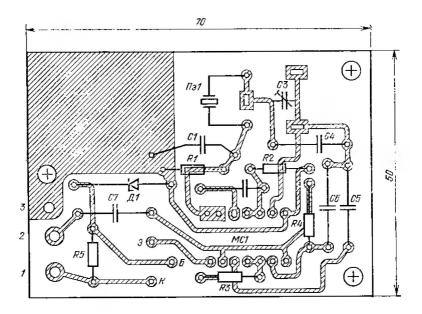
Печатная плата кварцевого калибратора с монтажной схемой (вид снизу)
